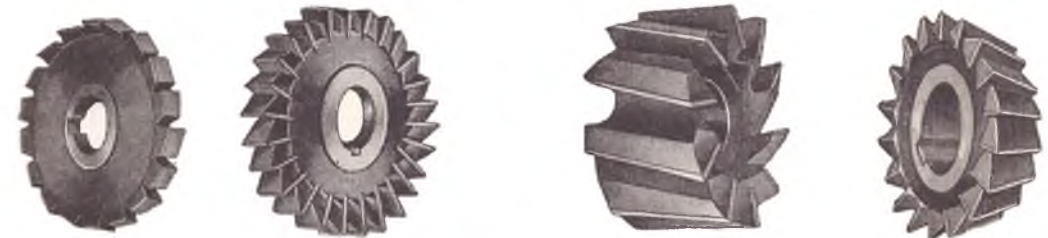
Фрезы для металлорезания дисковые: 1 — пазовая ватылочная; 2 — дисковая трехсторонняя с мелким зубом
